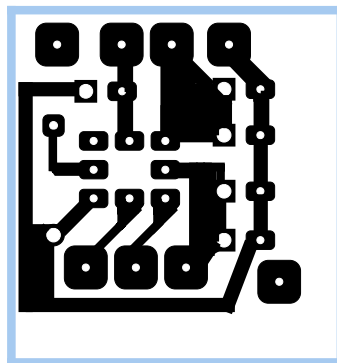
Placa do sensor - dimensões reais: 23mmX24,5 mm.
